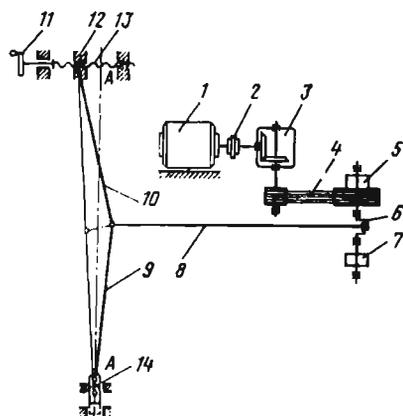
Кинематическая схема привода ползуна обсечного станка
